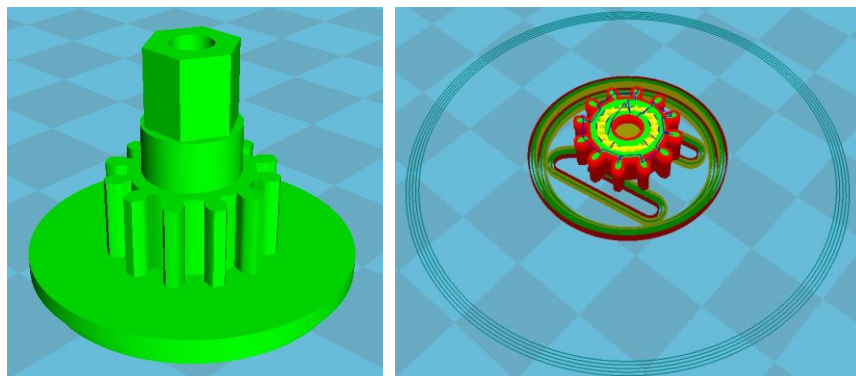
Posición de fabricación de la pieza dentada. Cura.
